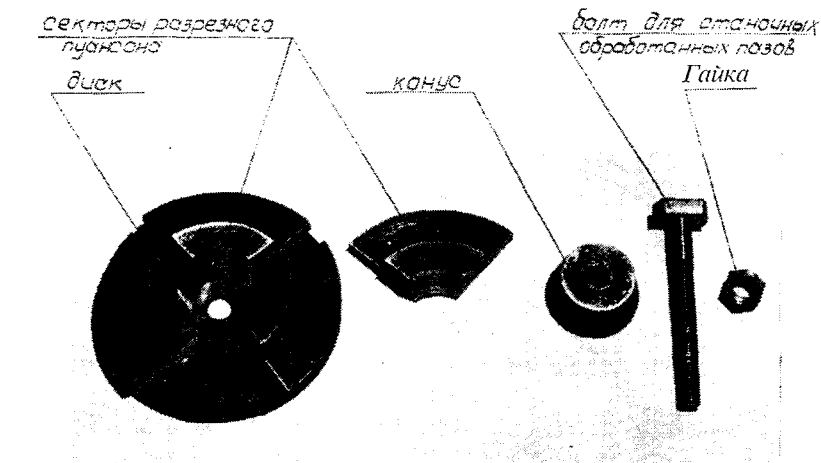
21. Внешний вид приспособления для сборки гофрированных демпферов
